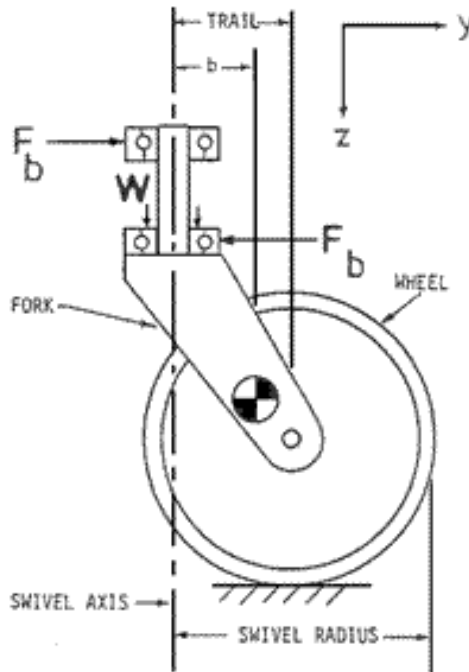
Esquema de rueda giratoria. F_b , fuerza de rodamiento; W , carga; b , dimensiones.²
